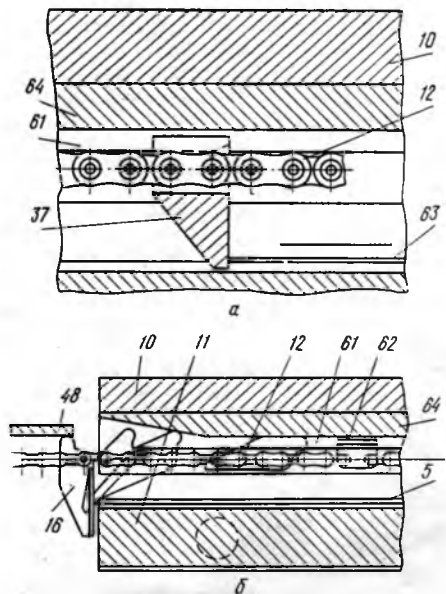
Схема работы цепного конвейера: а — охватывающего нижнюю плиту; б — верхнюю плиту
